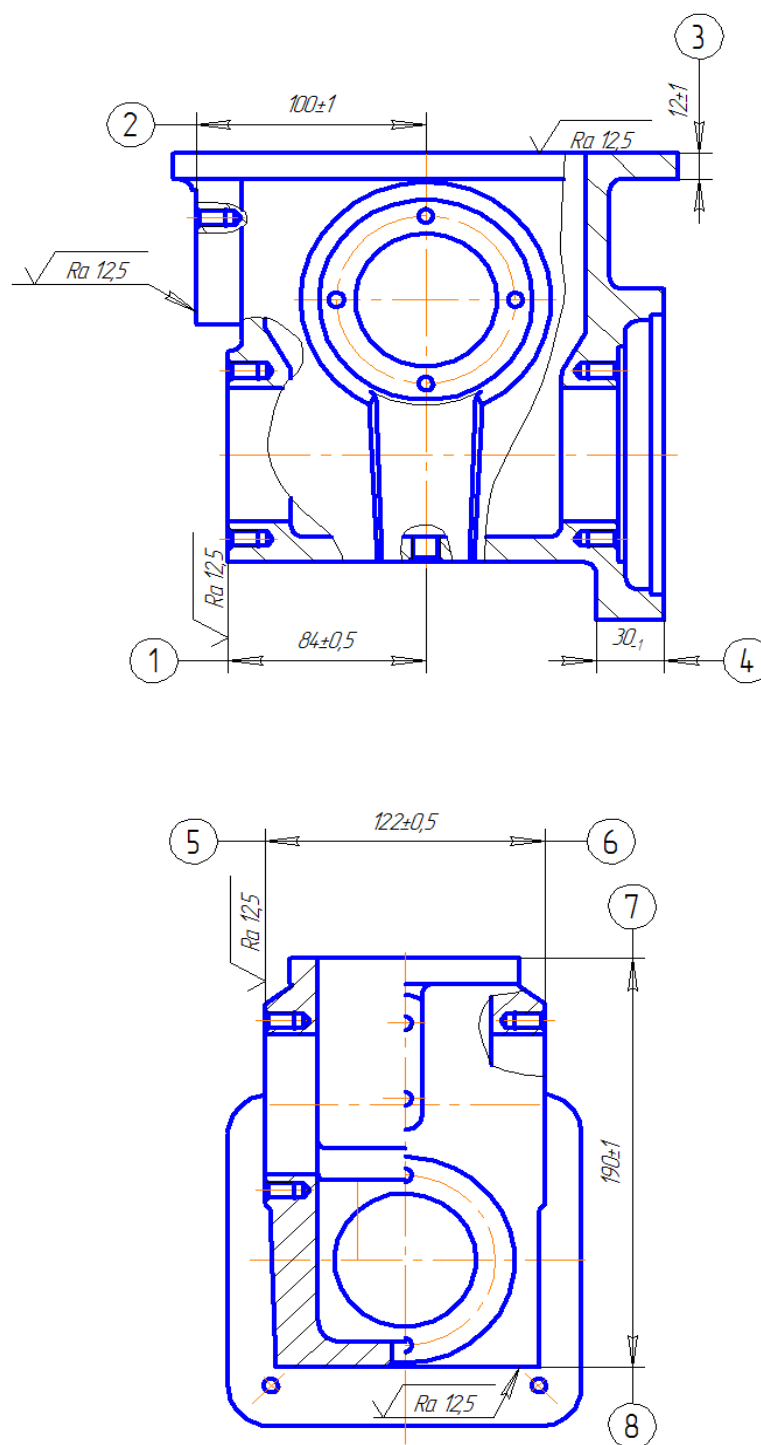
Эскиз детали «Корпус редуктора водяной помпы»
